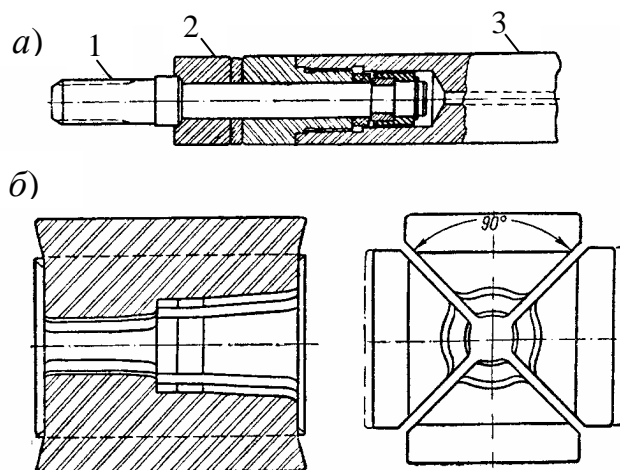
Общий вид составной оправки и рабочих кулачков для редуцирования внутренней поверхности корпуса муфты: *a* – составная оправка; 1 – внутренняя оправка; 2 – внешняя оправка; 3 – толкатель; *б* – рабочие кулачки
